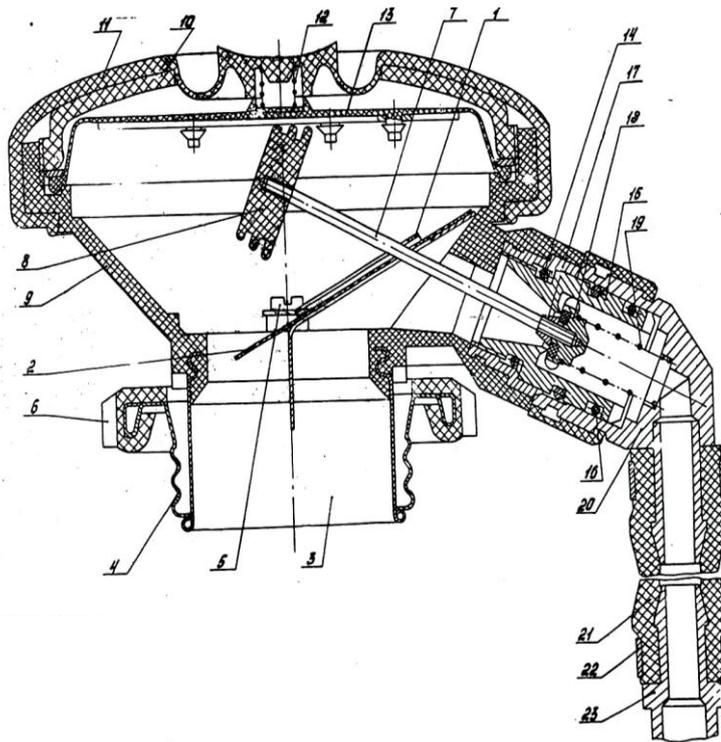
Легочный автомат: 1 – щиток; 2 – заслонка; 3 – штуцер; 4 – гайка; 5 – винт; 6 – облицовка; 7 – шток; 8,17 – втулка; 9 – корпус; 10 – гайка; 11 – обойма; 12 – пружина; 13 – мембрана; 14 – кольцо; 15 – седло; 16 – кольцо; 18 – клапан; 19 – пружина; 20 – корпус; 21 – соединительный рукав; 22 – кольцо; 23 – штуцер
